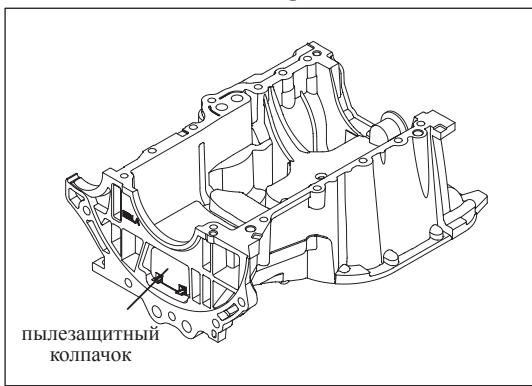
Установка пылезащитного колпачка нижней части блока цилиндров
